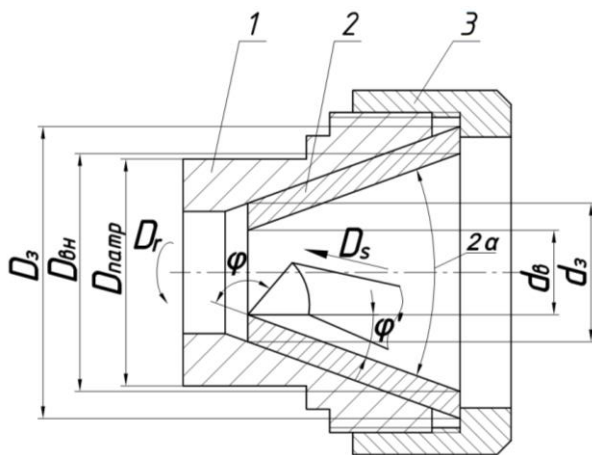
Процес розточування внутрішньої циліндричної поверхні дослідного зразка:
